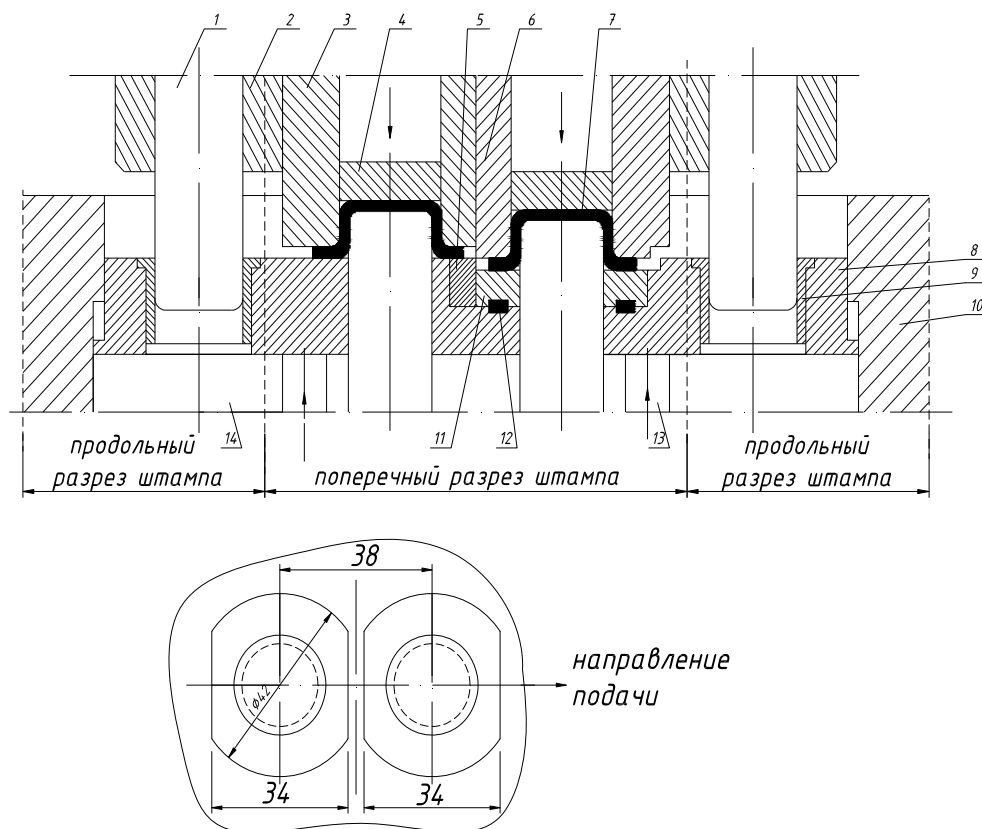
Штамп совмещенного действия для штамповки двух деталей
